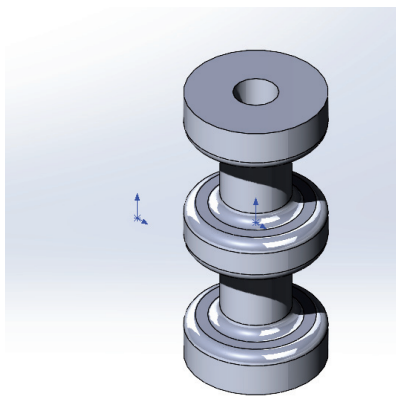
Расположение базовой детали в сборке относительно системы координат сборки
